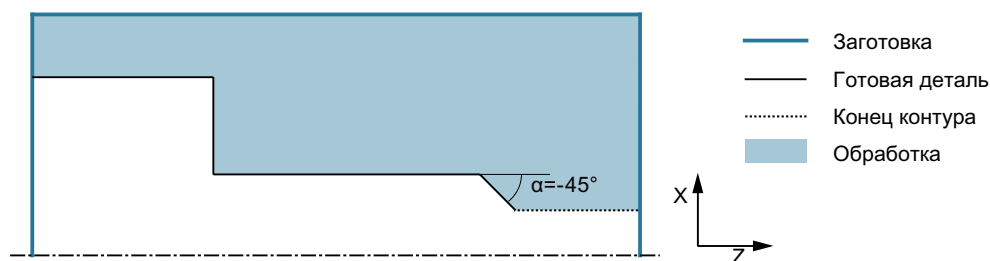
$\alpha \leq 1^\circ$: Завершение между заготовкой и готовой деталью сбоку
